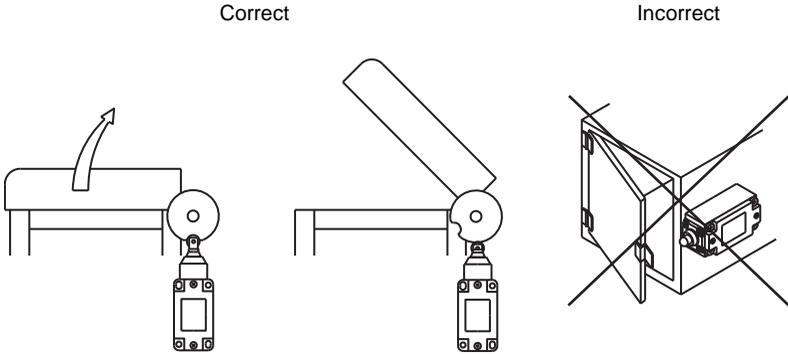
Exemple de montage pour un dispositif de protection pivotant
